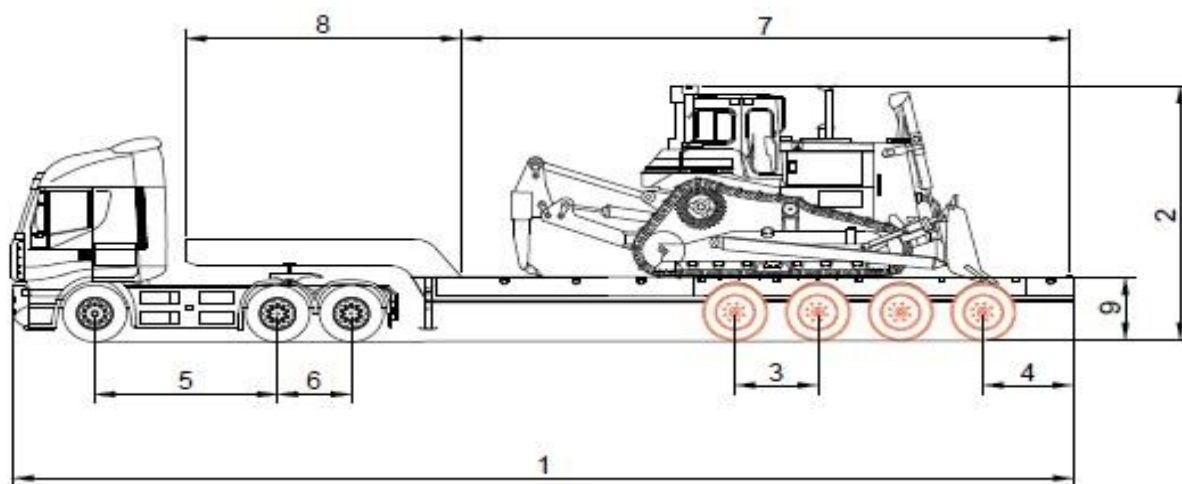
Pré-projeto do conjunto semirreboque e cavalo mecânico
